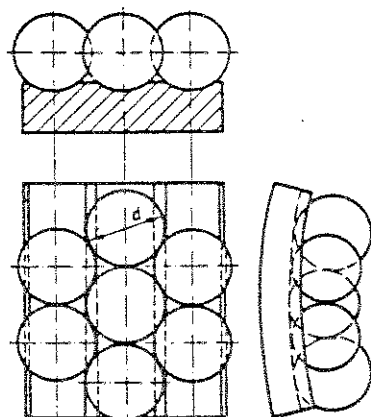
a. Hexagonale Packung der Mahlkugeln entlang der Rillenpanzerung
